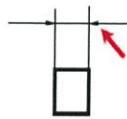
การบอกลักษณะภาพฉาย Dimension (1) [4]
